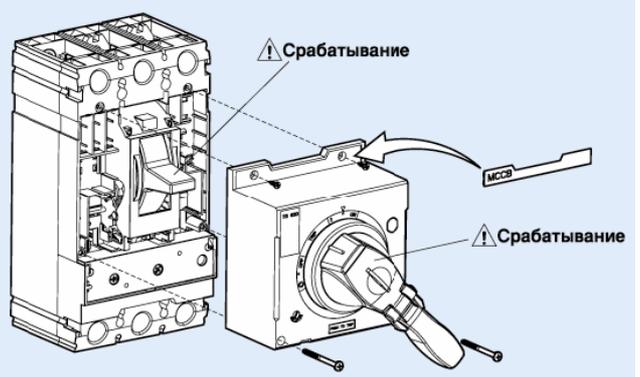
Габаритные и установочные размеры, способ установки стандартных поворотных рукояток TS400 и TS630
